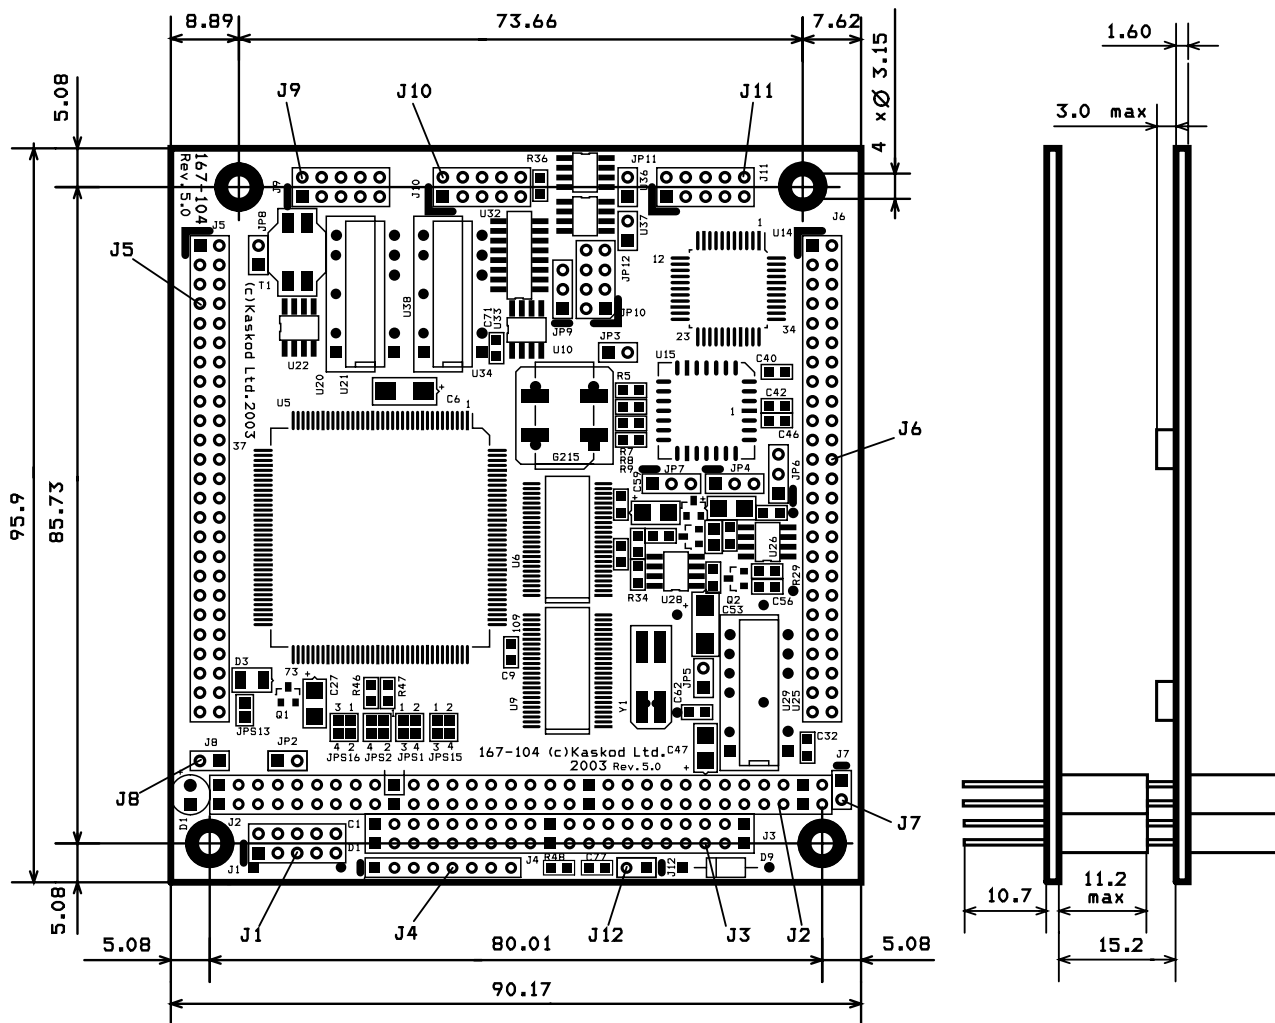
Габаритные и установочные размеры в миллиметрах.
